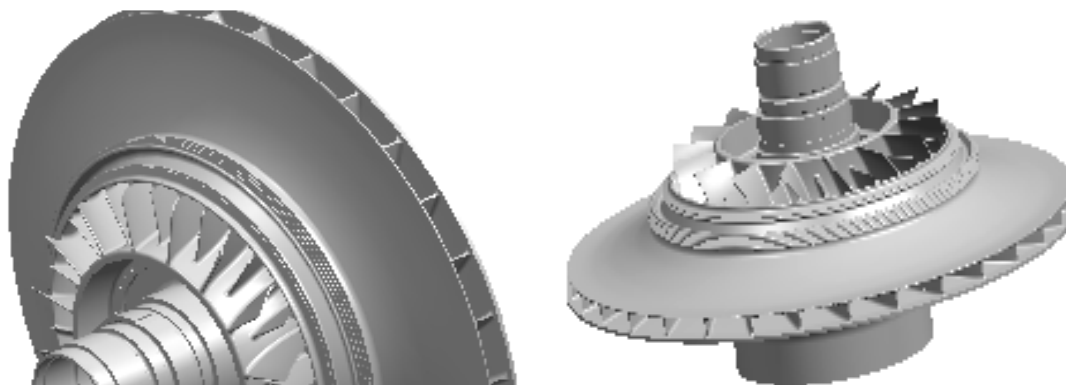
Виды готовой детали закрытого центробежного колеса с охлаждением покрывного диска
